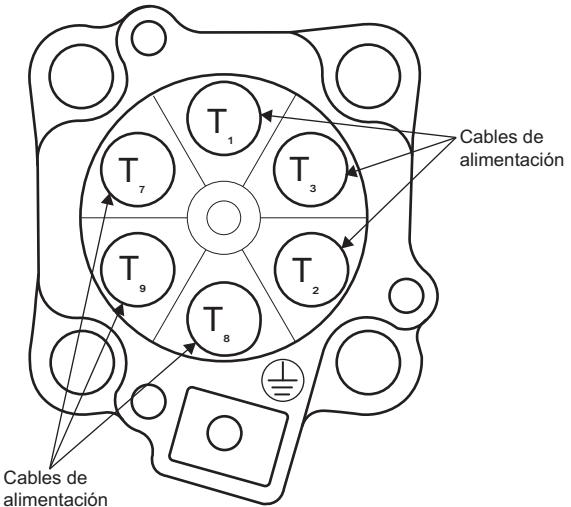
Disposición de Placa Terminal de Bobinado Parcial de 6 Pines
